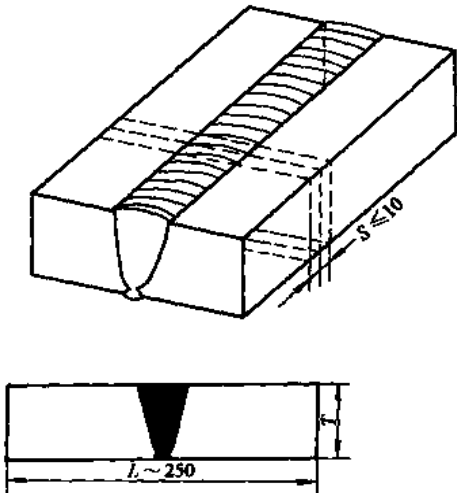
焊接接头全厚度侧向拉伸试样
